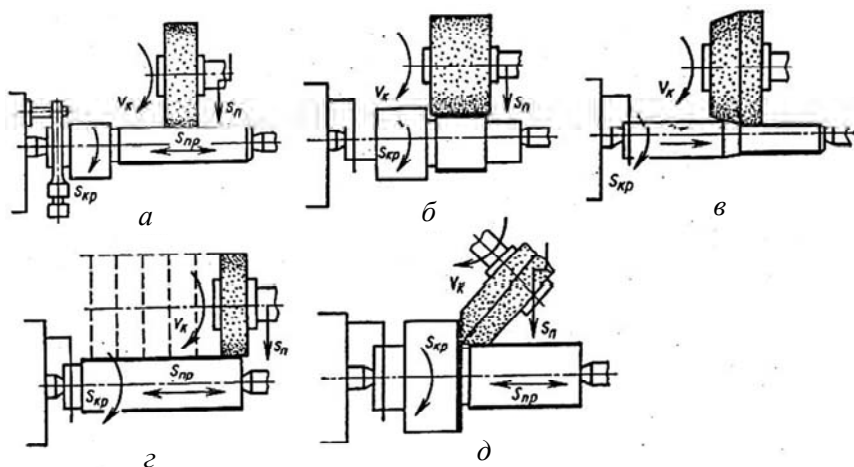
Схемы круглого и наружного шлифования цилиндрических поверхностей
